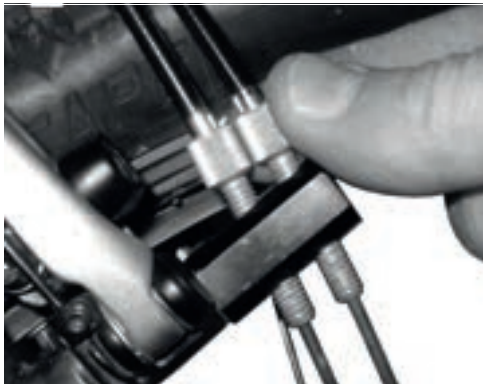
ROHLOFF-Naben Versionen mit interner Schaltansteuerung haben die Zugeinsteller am Zuggegenhalter
